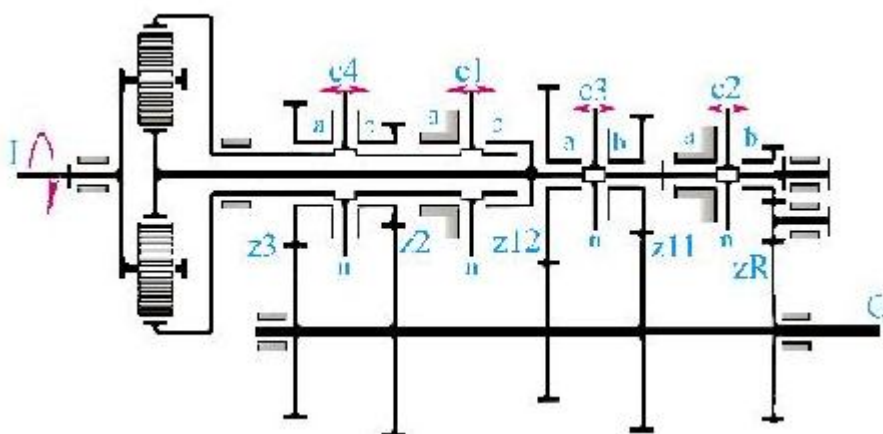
Кинематическая схема 12-ти ступенчатой коробки передач.
